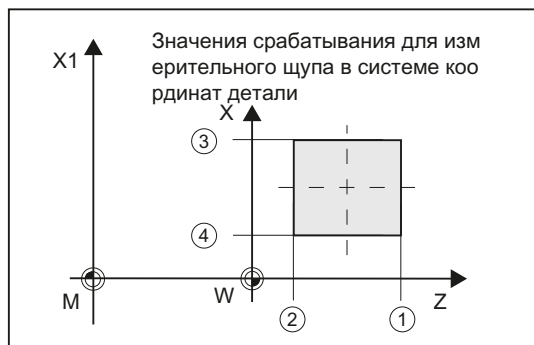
Измерительный щуп инструменты, по отношению к детали (G18)
